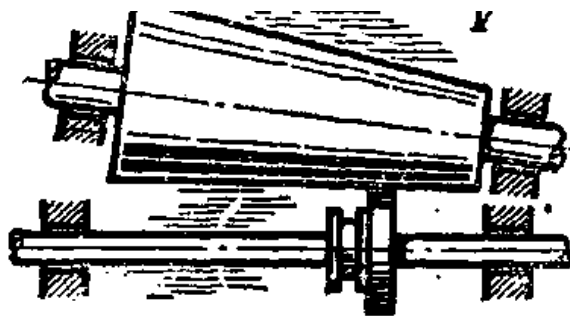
Загальний вигляд варіатора с пересувним циліндричним колесом
